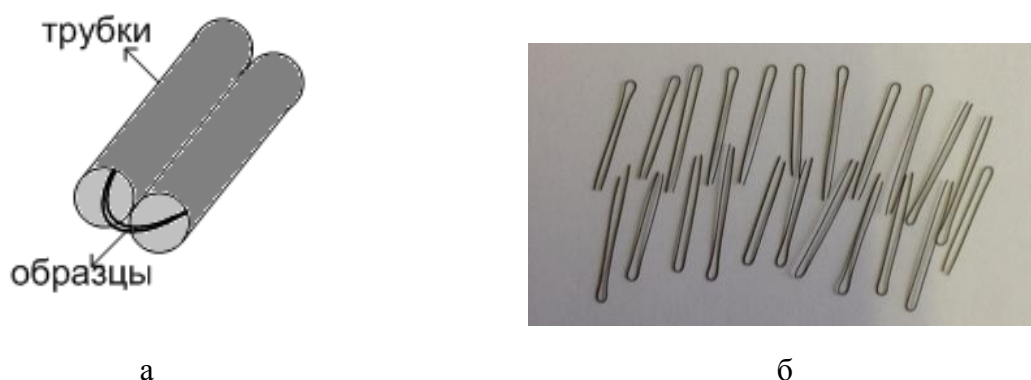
Изготовление образцов для испытаний на изгиб:
